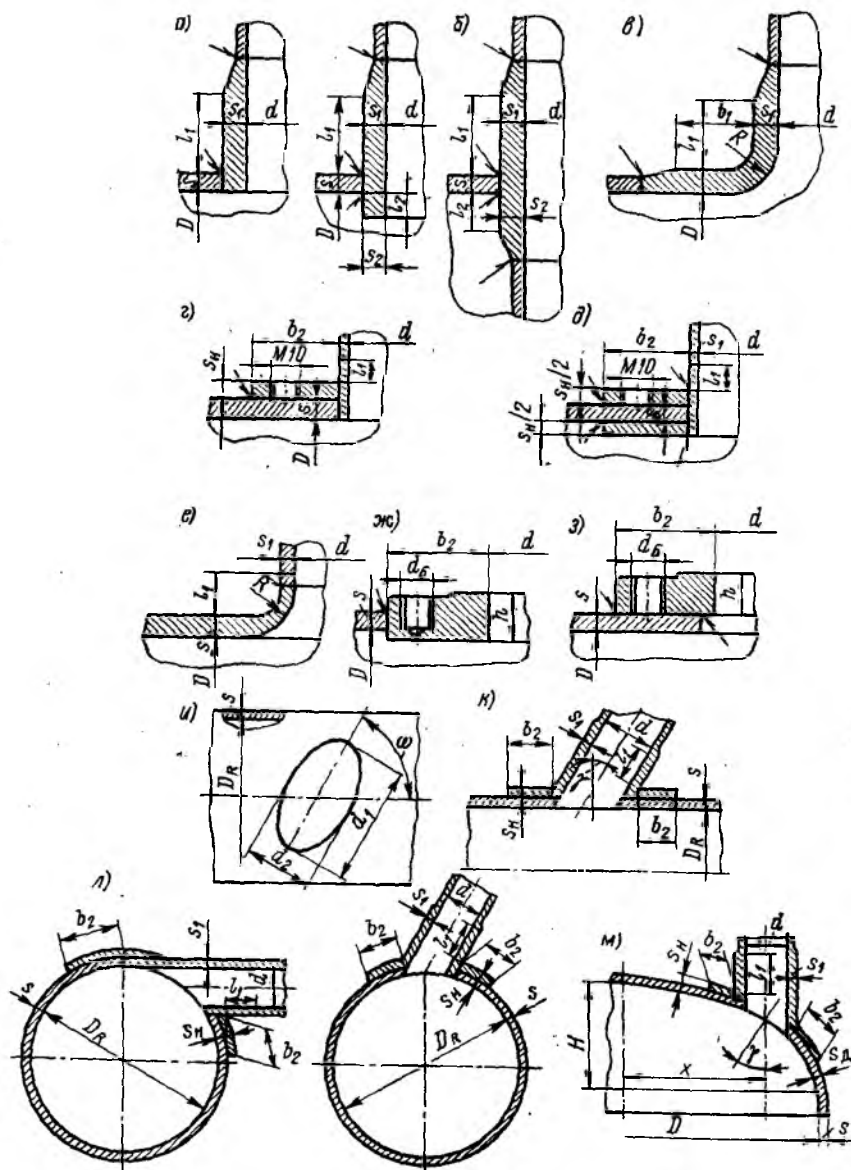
Конструкции укрепления отверстий в стенках аппаратов и днищ
